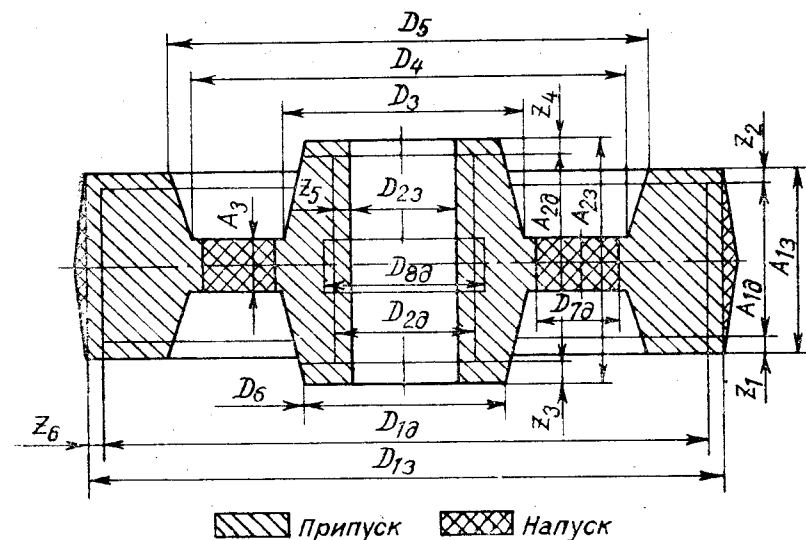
Заготовка шестерні. Розміри, напуски та припуски на оброблення різанням.
